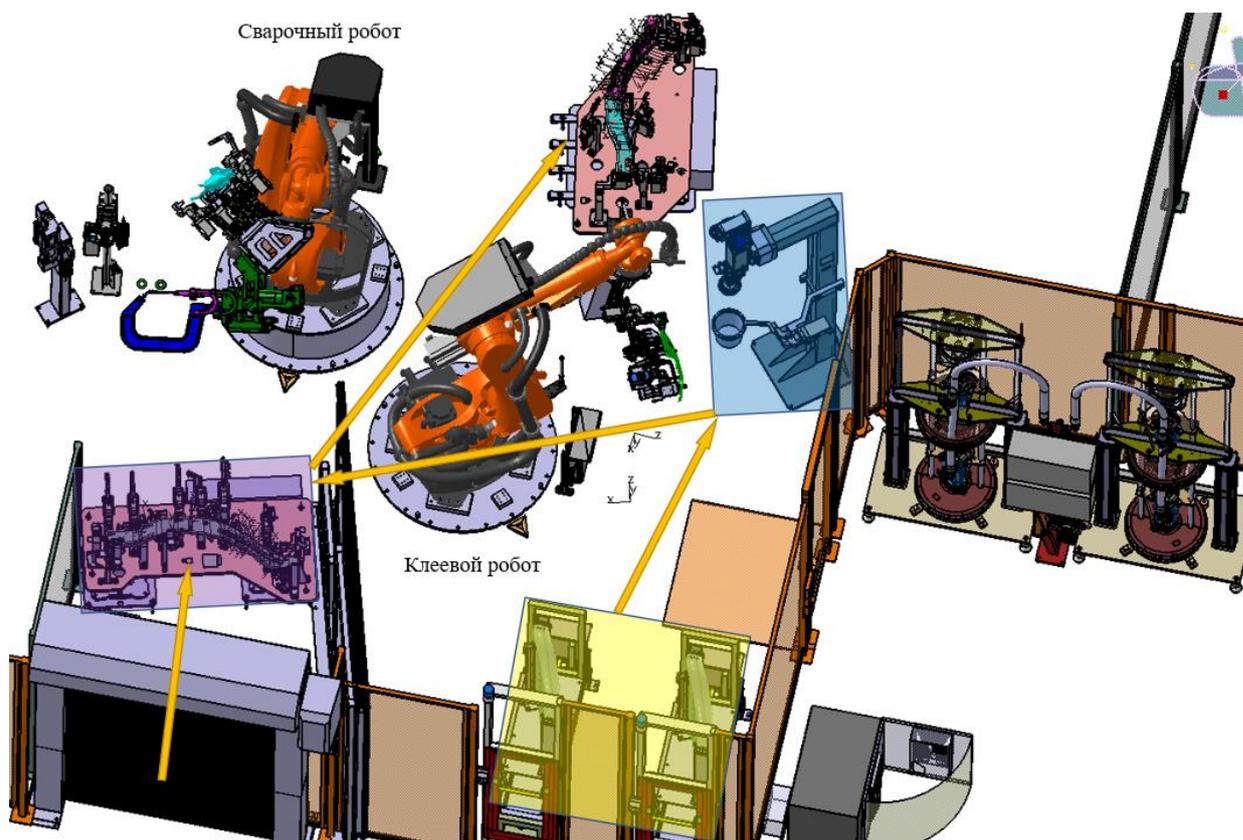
Общий вид положения сварочного и клеевого роботов
